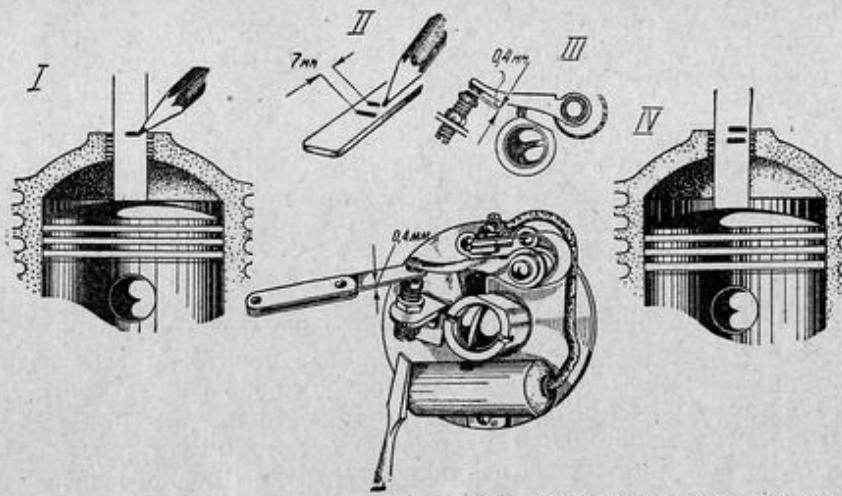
Регулировка зазора между контактами прерывателя и установка момента зажигания:
